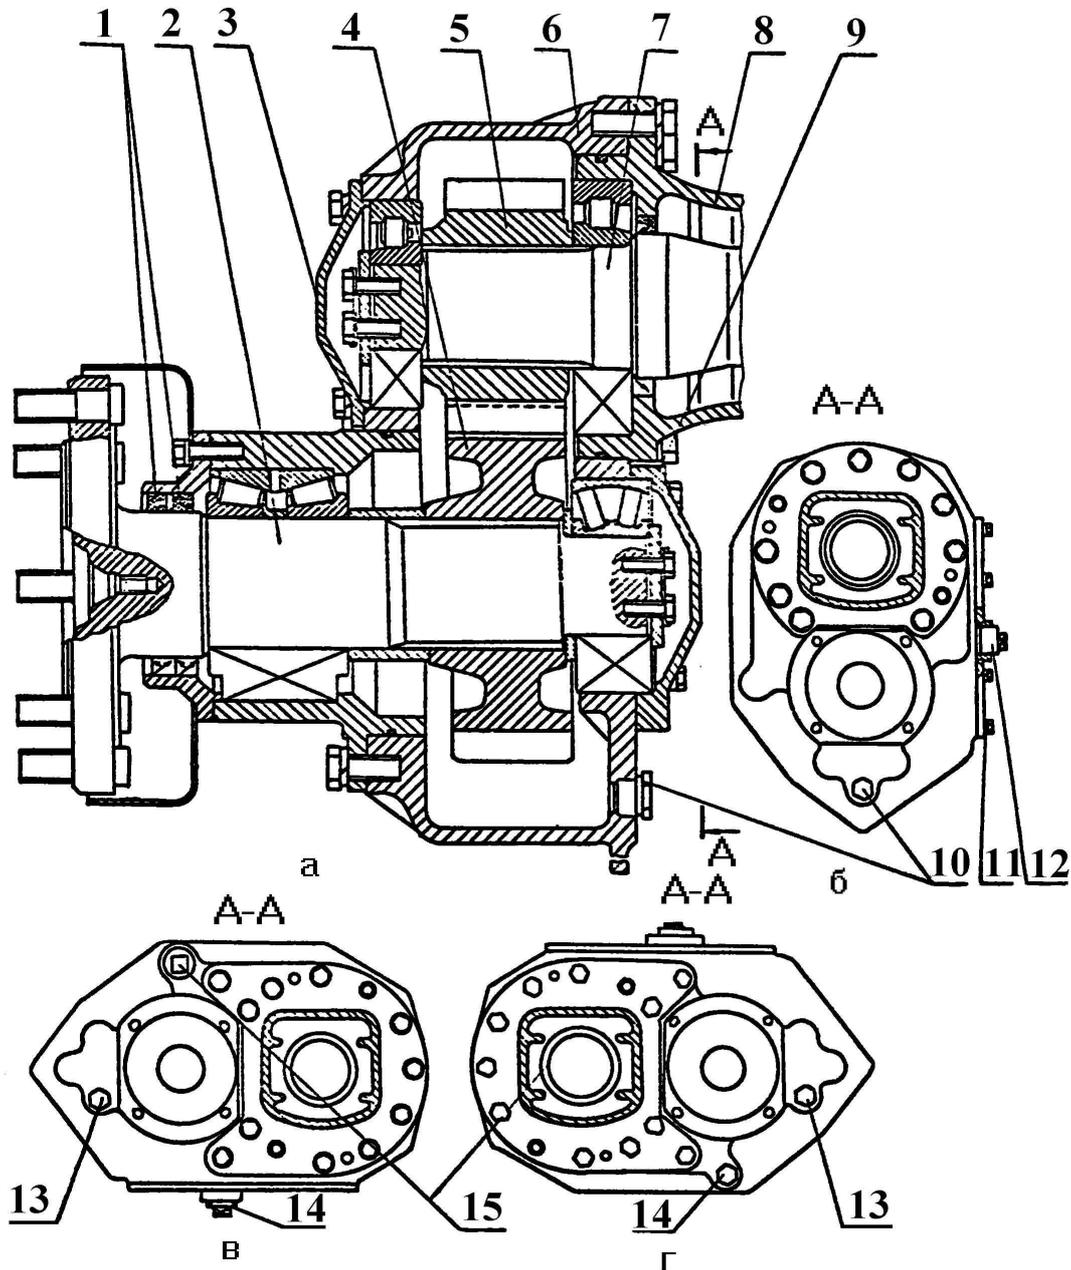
Конечная передача: 1 - манжеты; 2 - полуось; 3, 9, 11 - крышки; 4, 5 - шестерни; 6 - корпус; 7 - вал; 8 - рукав; 10, 14 - пробки сливные; 12, 15 - пробки маслозаливных отверстий; 13 - пробка контрольного отверстия; а - редуктор (поперечный разрез); б - вид на редуктор переднего моста; в - вид на левый редуктор заднего моста; г - вид на
